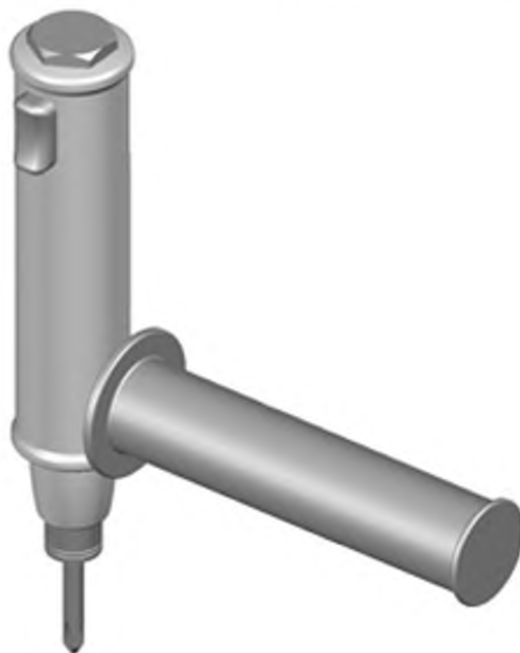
Шуруповерт с поддерживающей рукояткой
